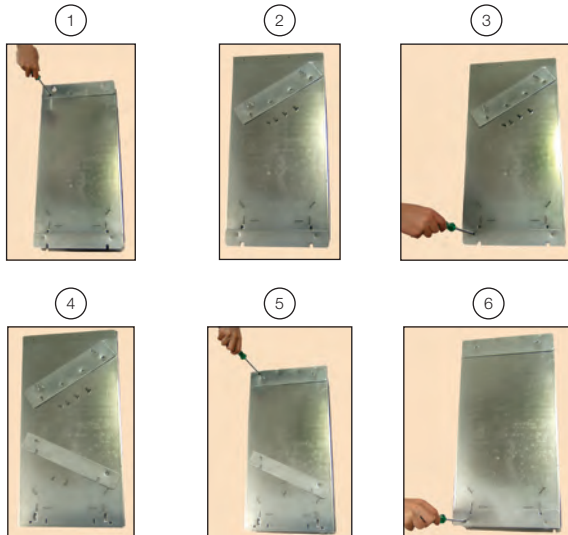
Reposicione os suportes de montagem nas mecânicas A a E. Nas mecânicas F, G e H os suportes devem ser removidos
